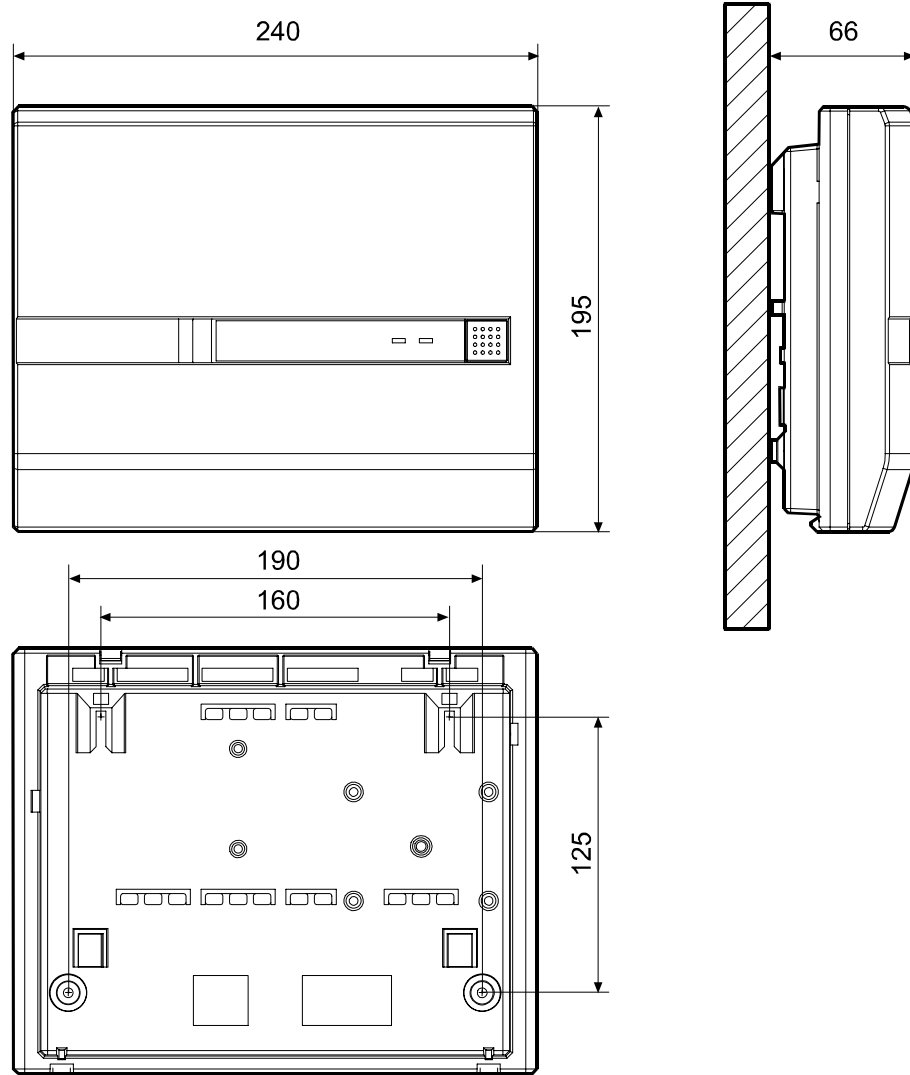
Габаритные размеры контроллера «Кронверк АТ+».
